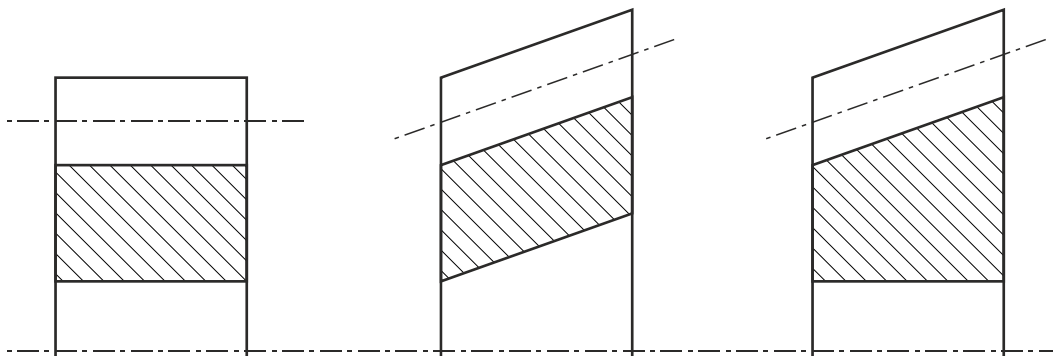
Skizzen der WNV: Zylinderrad (links), konische Bohrung am Beveloidrad (Mitte), zylindrische Bohrung am Beveloidrad (rechts)
